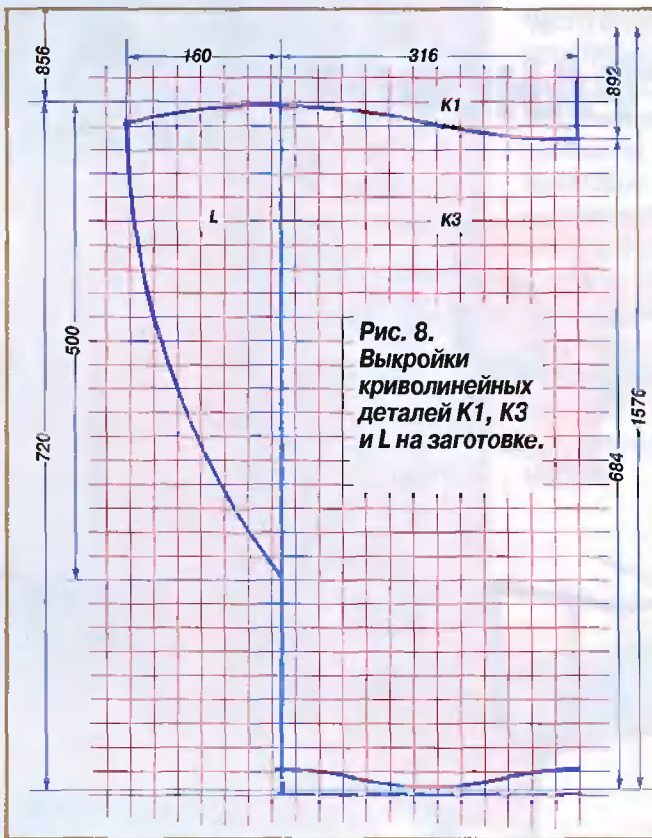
Выкройки криволинейных деталей K1, K3 и L на заготовке.
